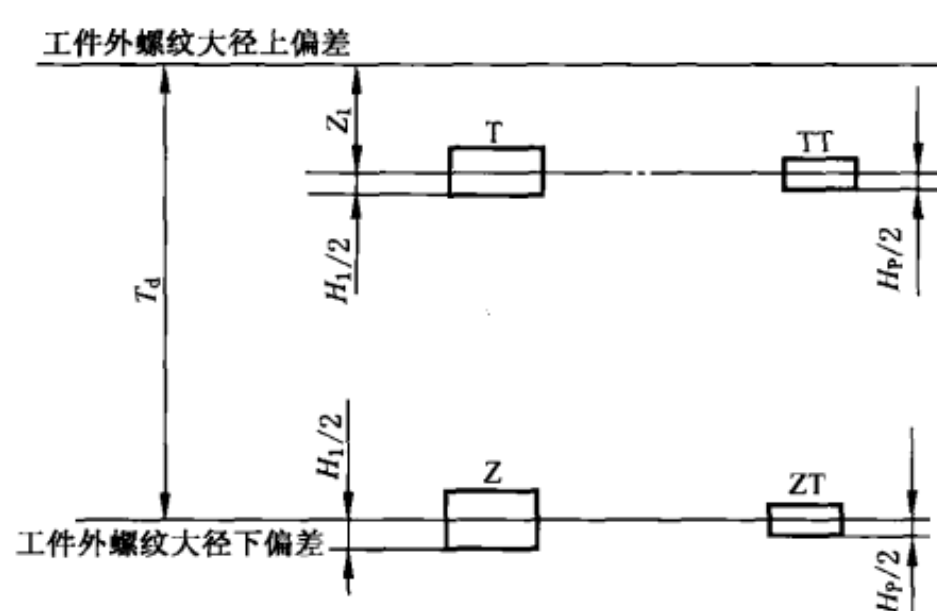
光滑环规或卡规直径的公差带位置
